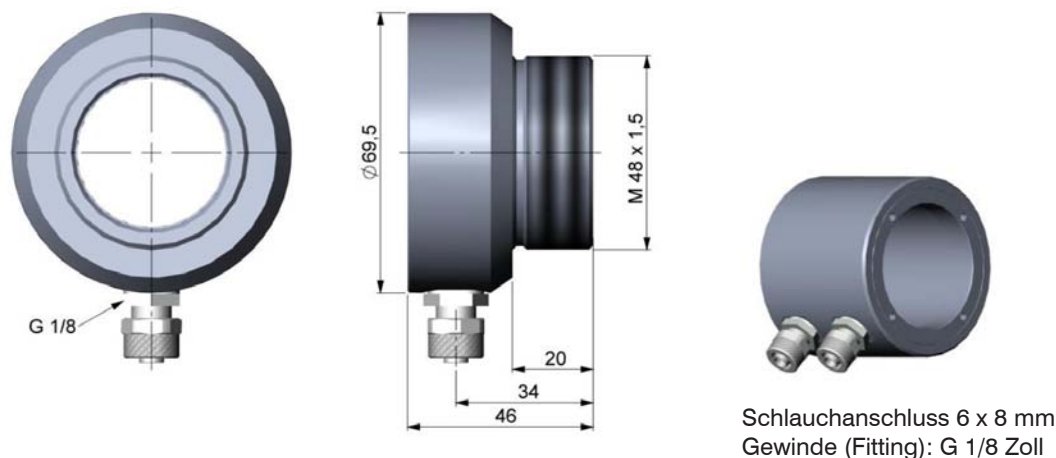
Wasserkühlgehäuse (TM-W-CTL)
